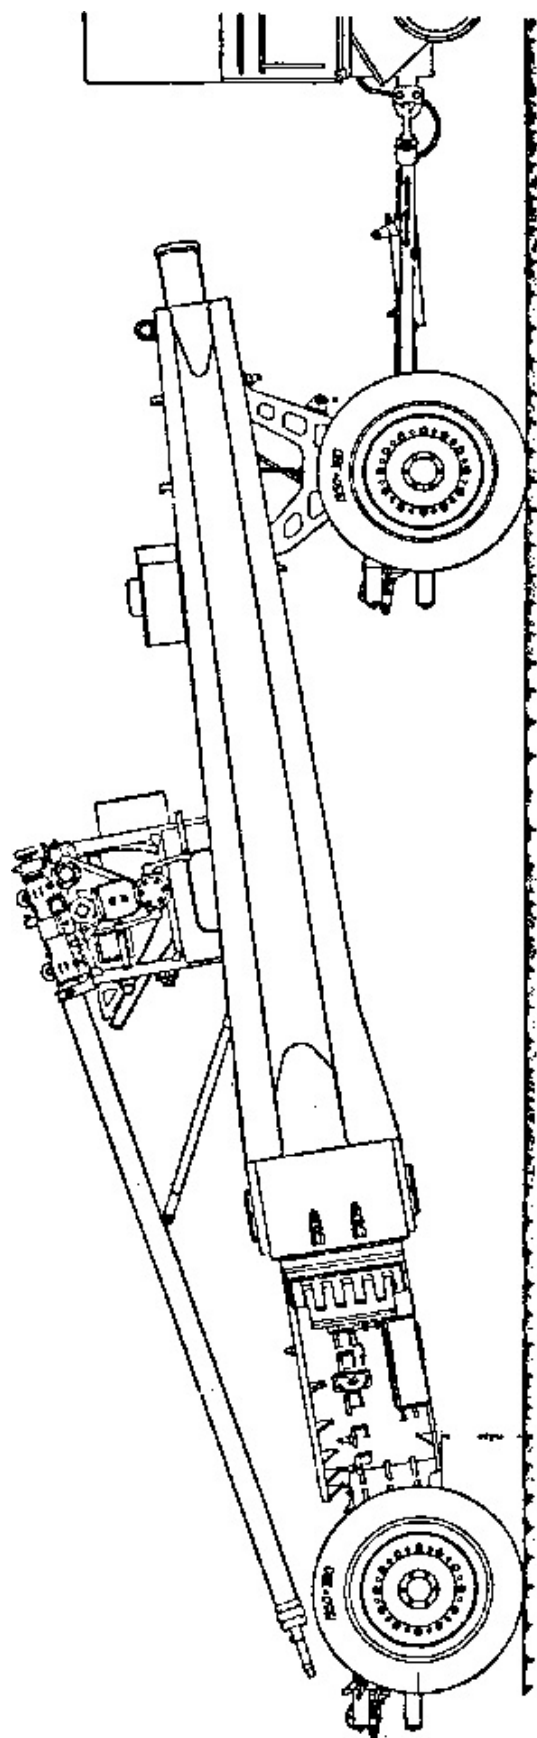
Повозка нижнего станка для пушки С-72 и гаубицы С-73
